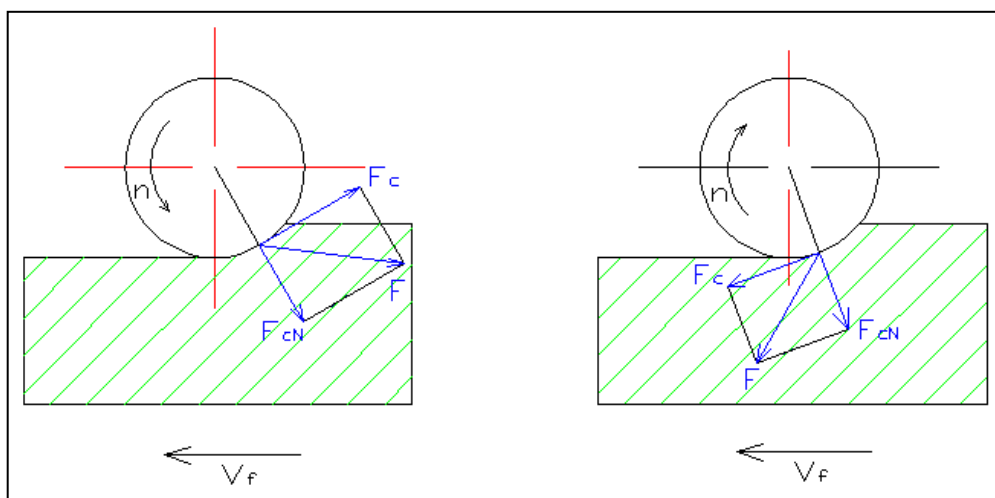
Záběrové pole frézování válcovou frézou [5].
